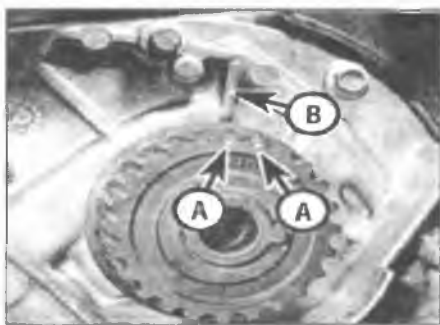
Установочные точки (А) на звездочке коленчатого вала должны располагаться по обеим сторонам ребра (В) на корпусе масляного насоса
